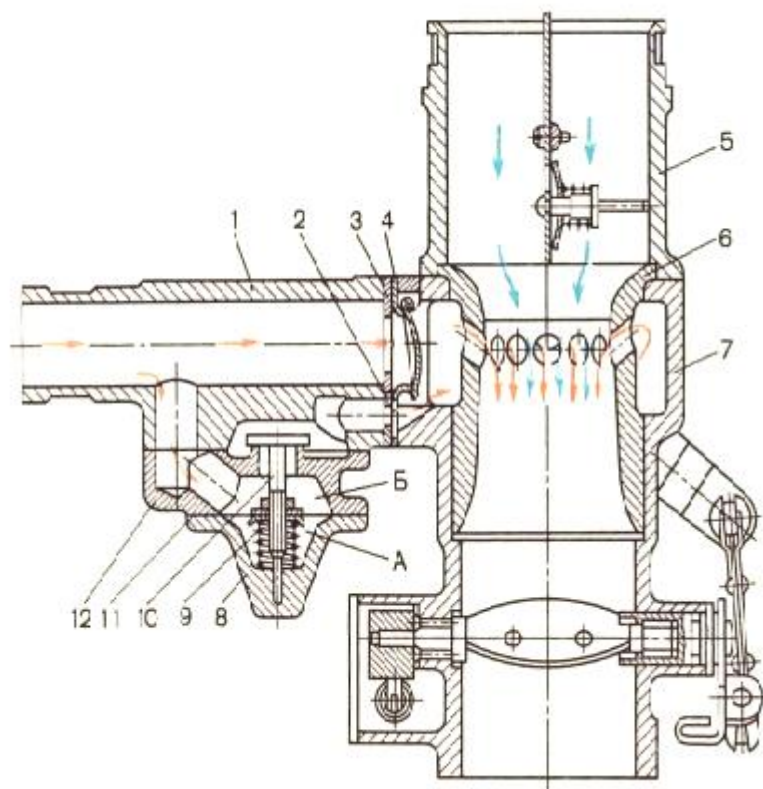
Газовоздушный смеситель автомобильного типа:
